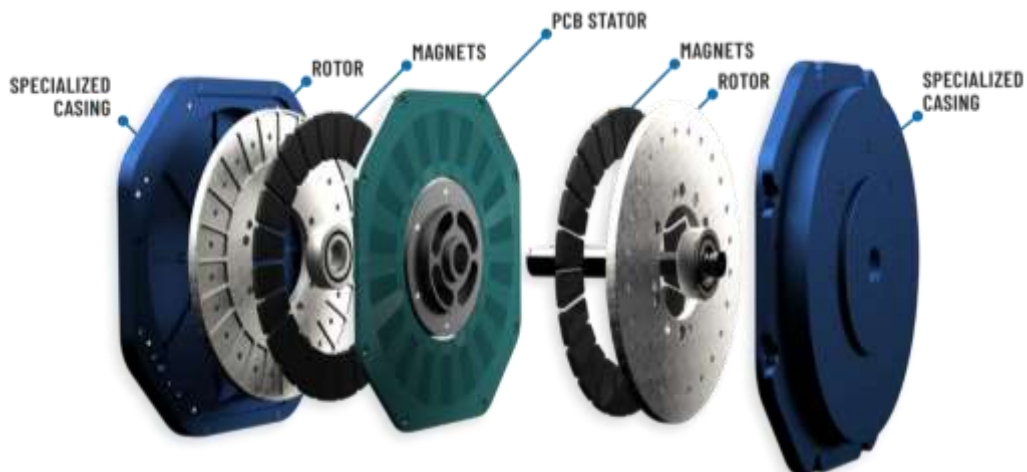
Разбор двигателя компании ECM PCB Stator Tech
